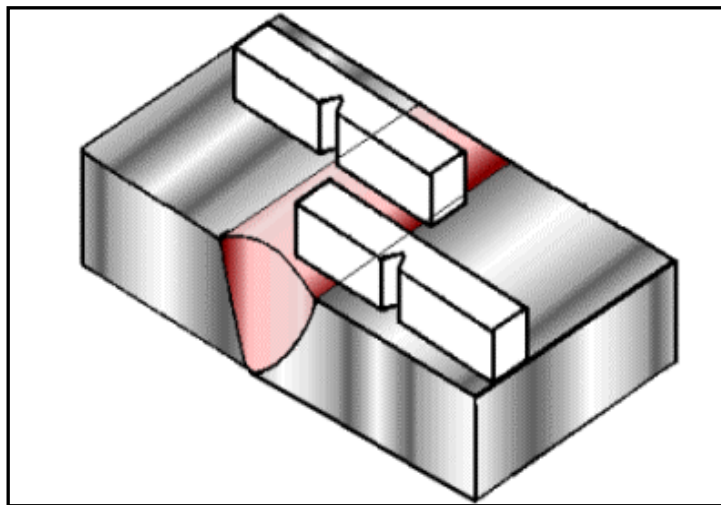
localisation des éprouvettes dans un joint soudé
